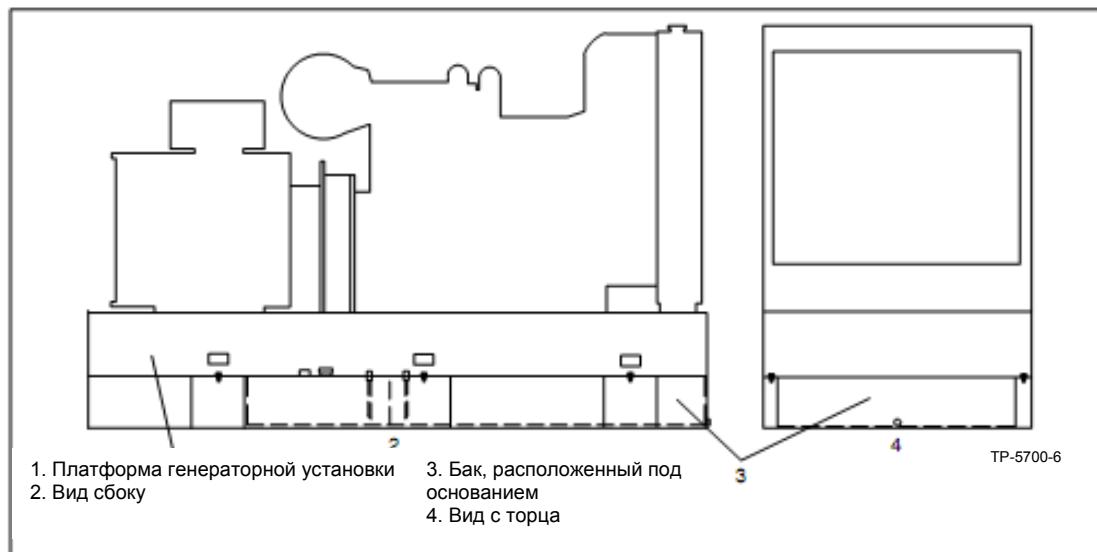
Топливный бак, расположенный под основанием генераторной установки
